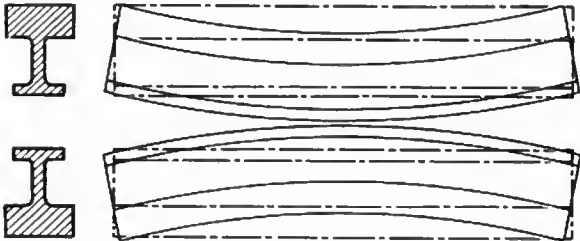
Voilage longitudinal selon la position de la poutre
